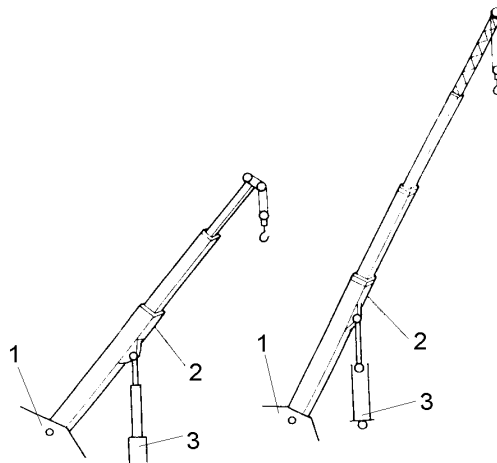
Стреловое оборудование с жесткой подвеской
